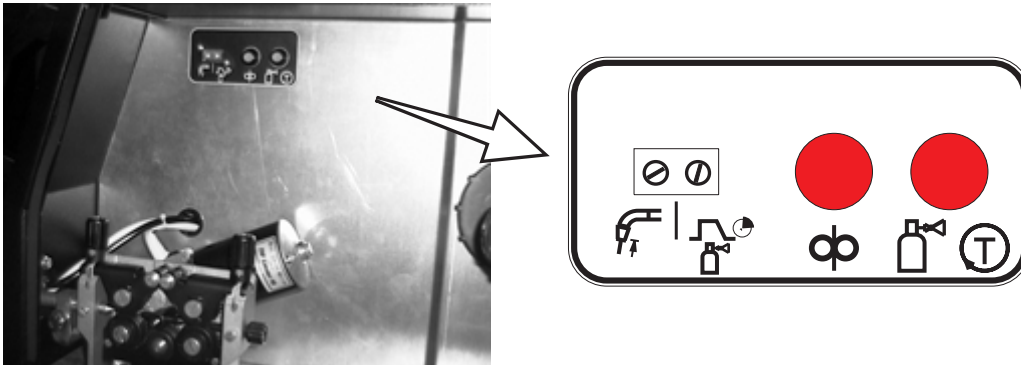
/2: Bedienelemente im Inneren des Schweißgerätes bzw. DV- Koffer
